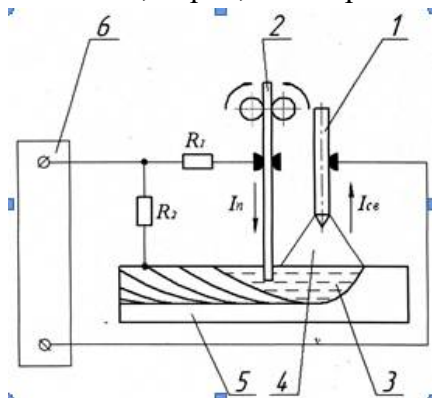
Схема процесу зварювання: 1 – електродний дріт; 2 – присадочний дріт; 3 – зварна ванна; 4 – зварна дуга; 5 – виріб; 6 – джерело живлення
